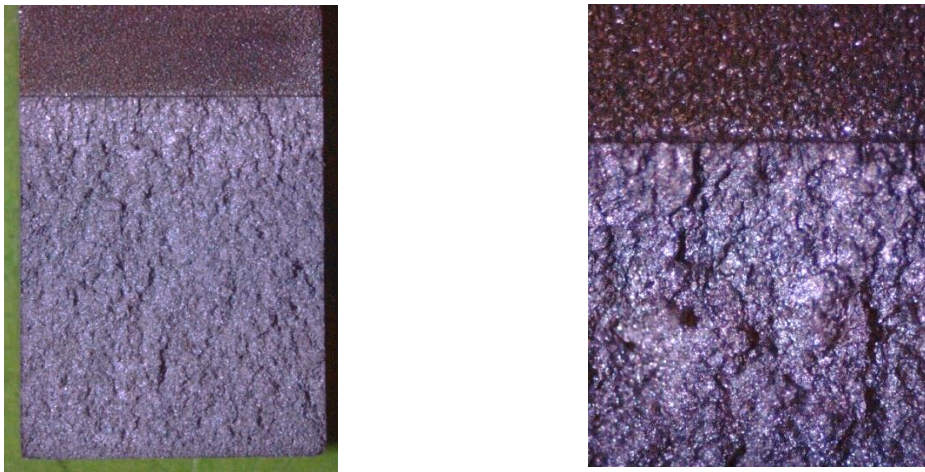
Tipología superficie de fractura, aspecto granular en la zona de fractura final
